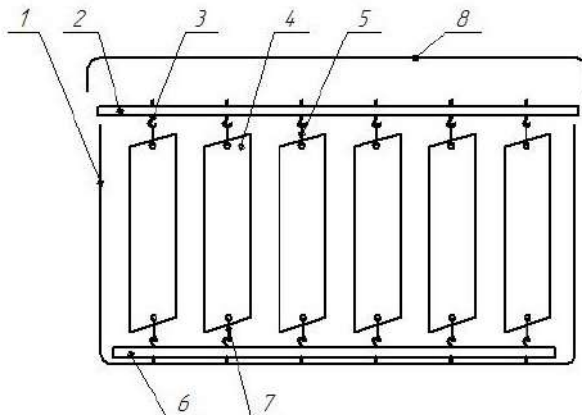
Контейнер для перевозки испытуемых немагнитных образцов с противокоррозионными защитными невысыхающими покрытиями: 1 – контейнер, 2 – верхняя планка, 3 – крючок, 4 – образец, 5 – подвязка верхняя, 6 – нижняя планка, 7 – подвязка нижняя, крышка.
